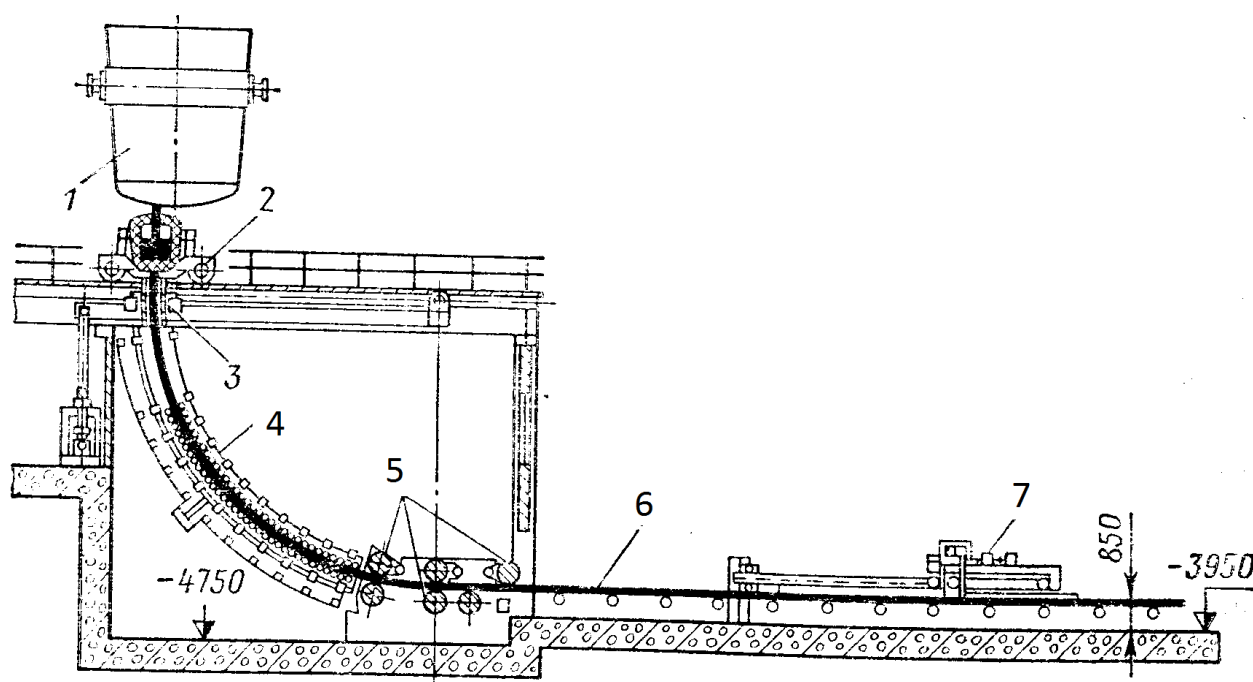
Схема устройства МНЛЗ радиального типа: 1-ковш, 2-разливочное устройство, 3-водоохлаждаемый кристаллизатор, 4-зона вторичного охлаждения, 5-тянущие валки, 6-слиток, 7-газорез.
